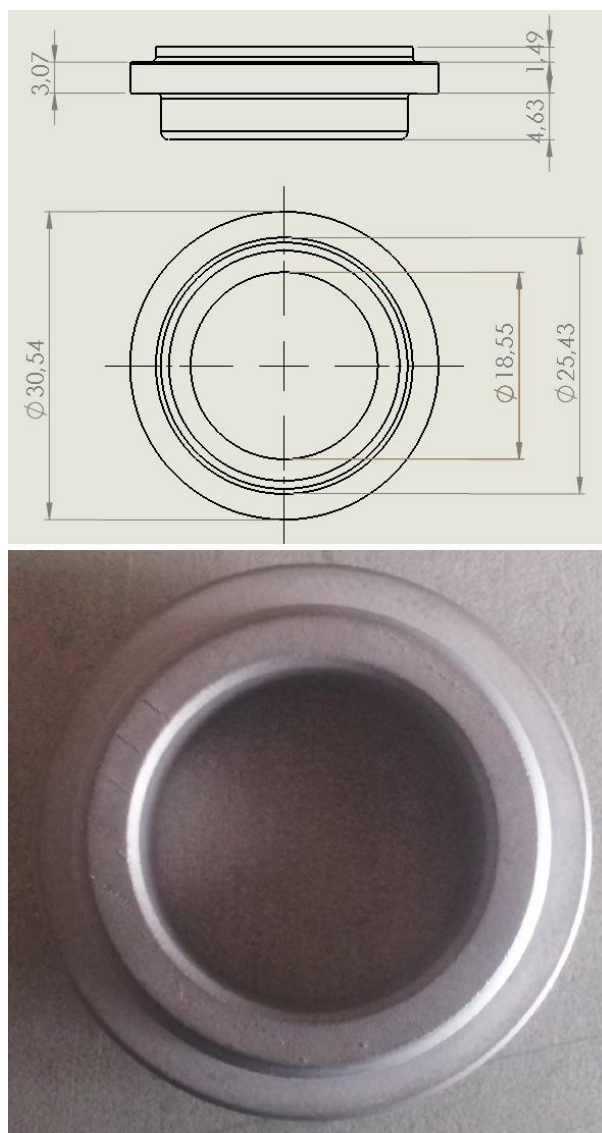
Desenho técnico dos vedantes e o seu aspeto no estado inicial
